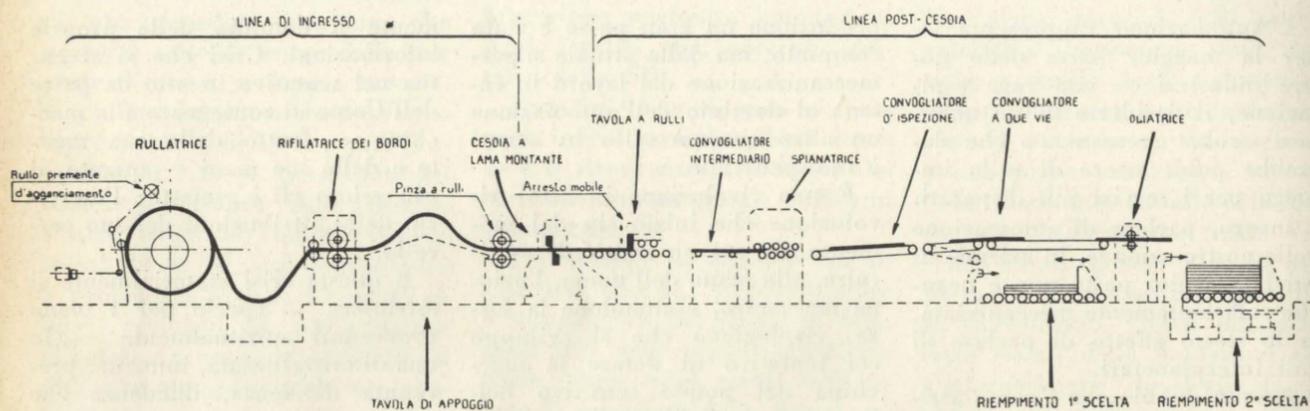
Equipaggiamento di comando di una linea per il taglio delle lamiere.
